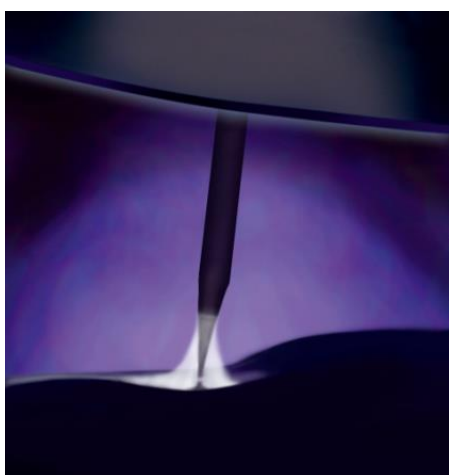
Сильно сжатая дуга обеспечивает качественную сварку корня.
